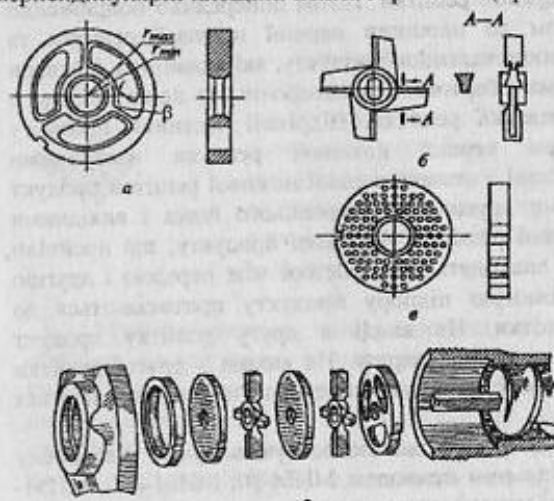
Ріжучі інструменти м'ясорубки: а – нерухома підрізна решітка; б – двосторонній ніж, що обертається; в – решітка ножова; г – основний набір ріжучих інструментів
